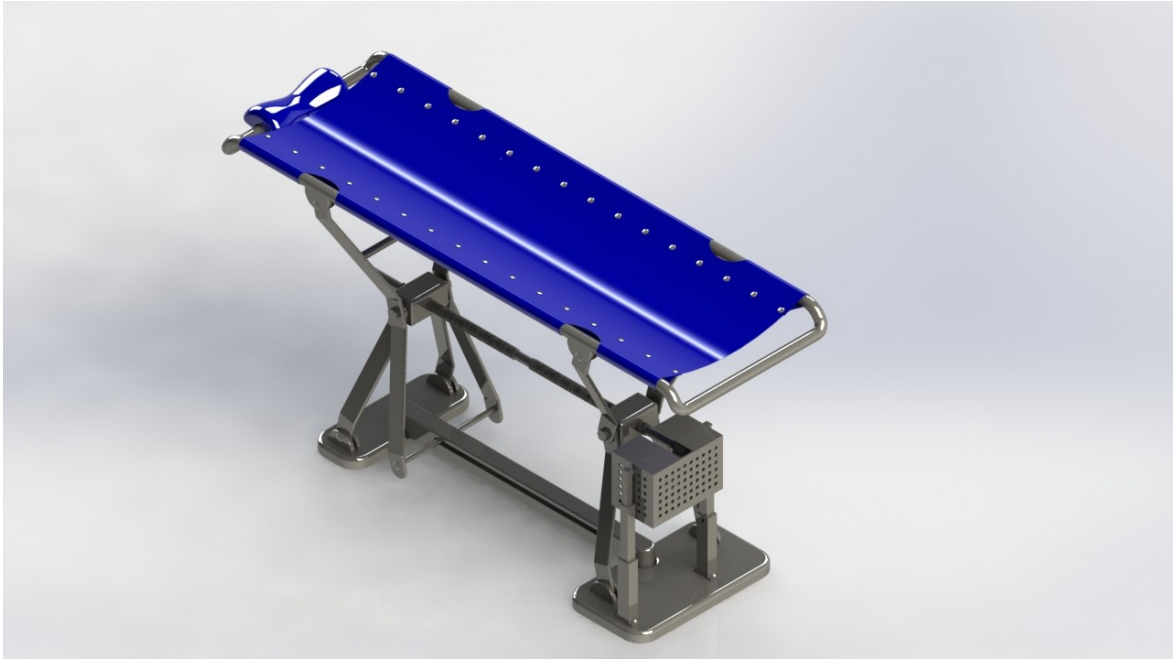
Conceito Final – Imagem de Pormenor do apoio de cabeça
